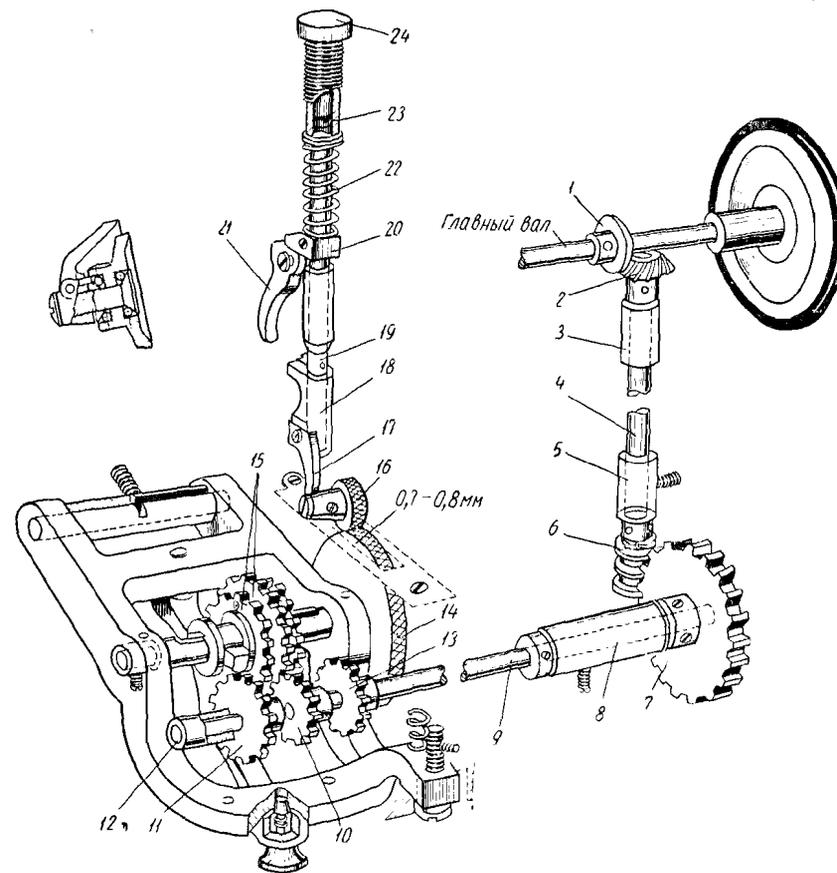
Механизм транспортера машины 34-го класса ПМЗ
